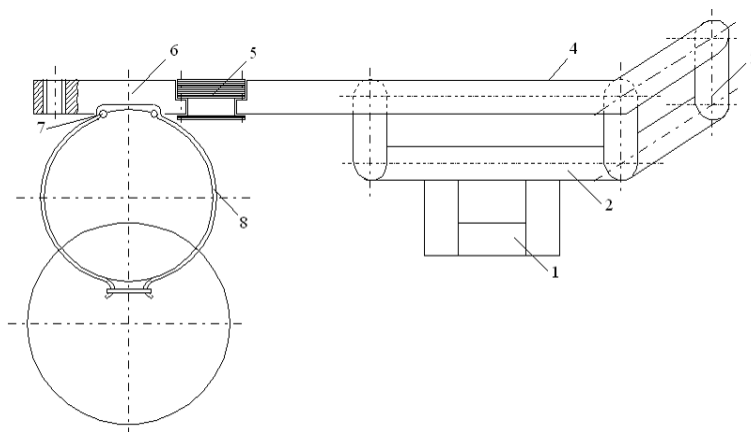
Ескіз технологічного оснащення для зміцнення деталей: 1 – основа; 2 – опорна напрямна; 3 – штанга; 4 – рухома направляюча; 5 – пластинчаста пружина; 6 – електродотримач; 7 – опорні ролики; 8 – фіксуєчий хомут
